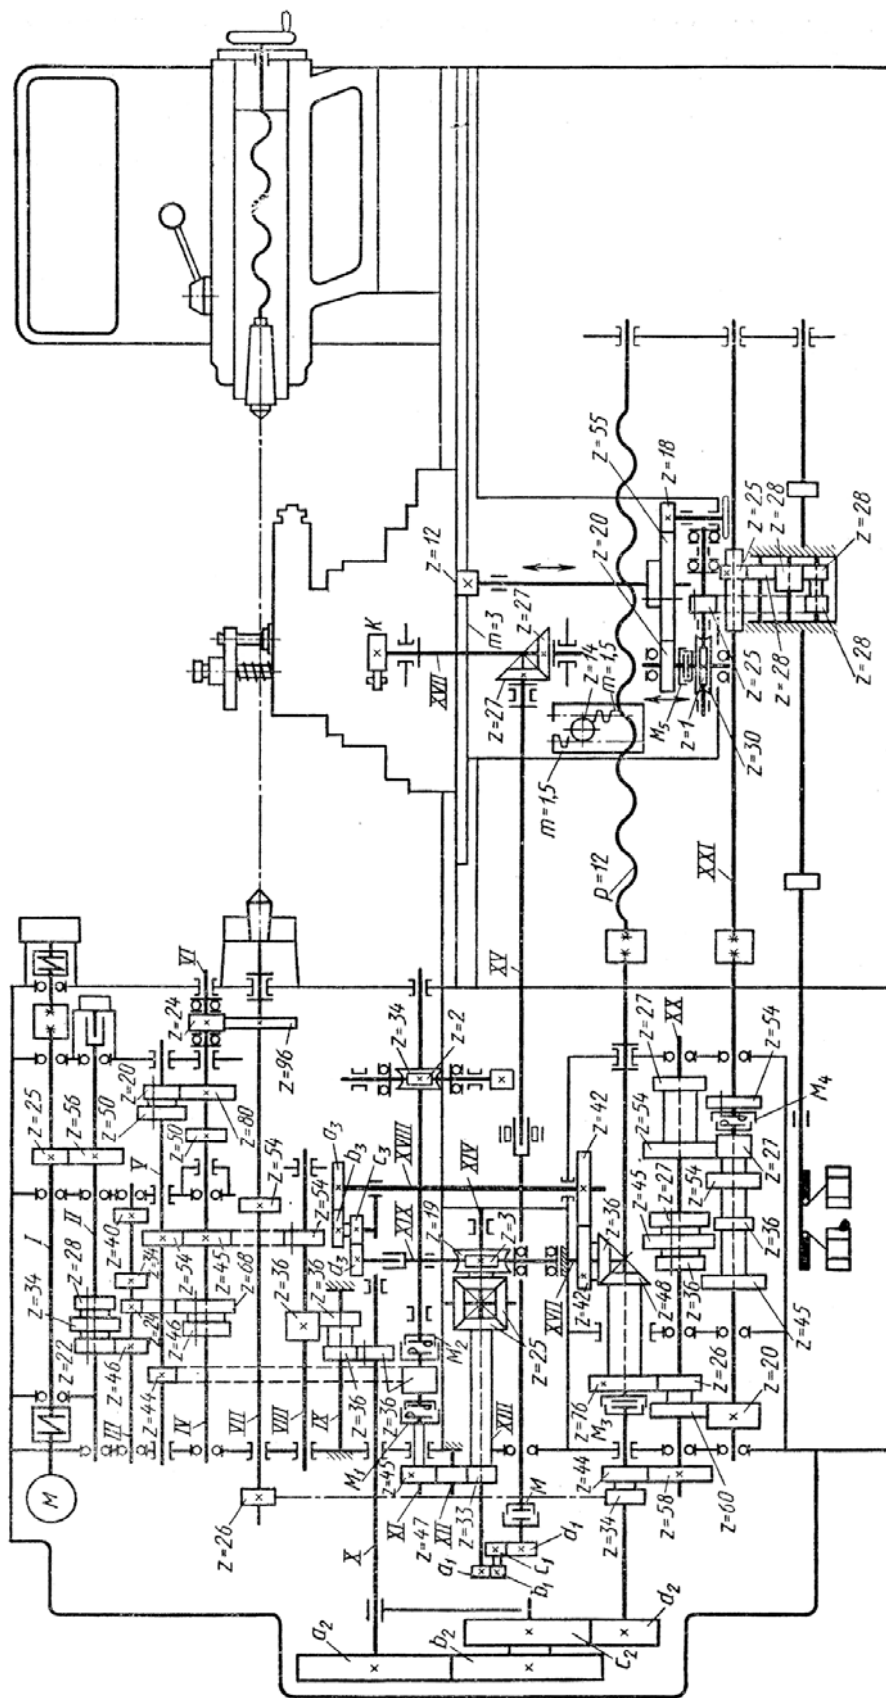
Кинематическая схема универсального токарно-затыловочного станка 1Б811
